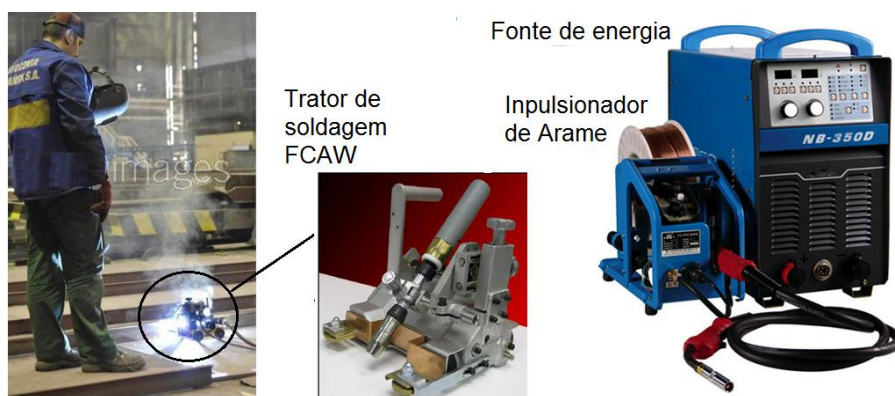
Esquema de soldagem FCAW, em ângulo, automatizada. Web ajustada (2016)
